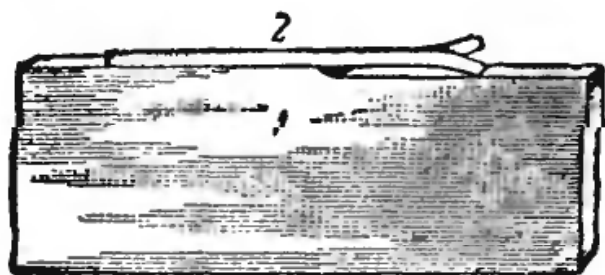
Шаблон для проверки развода зубьев: 1 — металлическая пластинка с выемкой, соответствующей величине проверяемого развода; 2 — полотно пилы.
